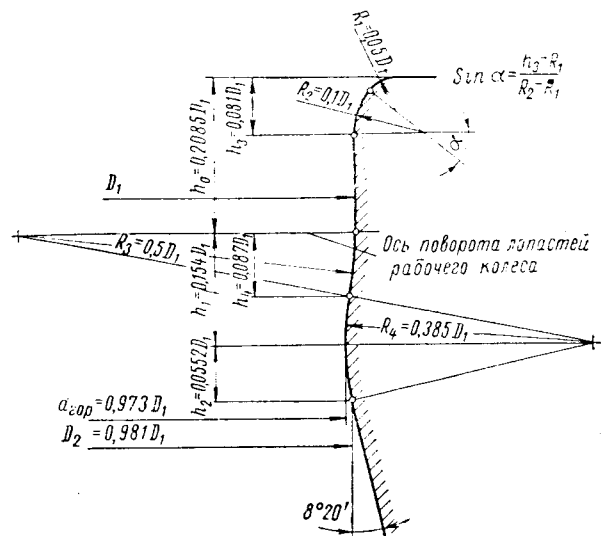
Размеры камеры рабочего колеса поворотлопастной гидротурбины
